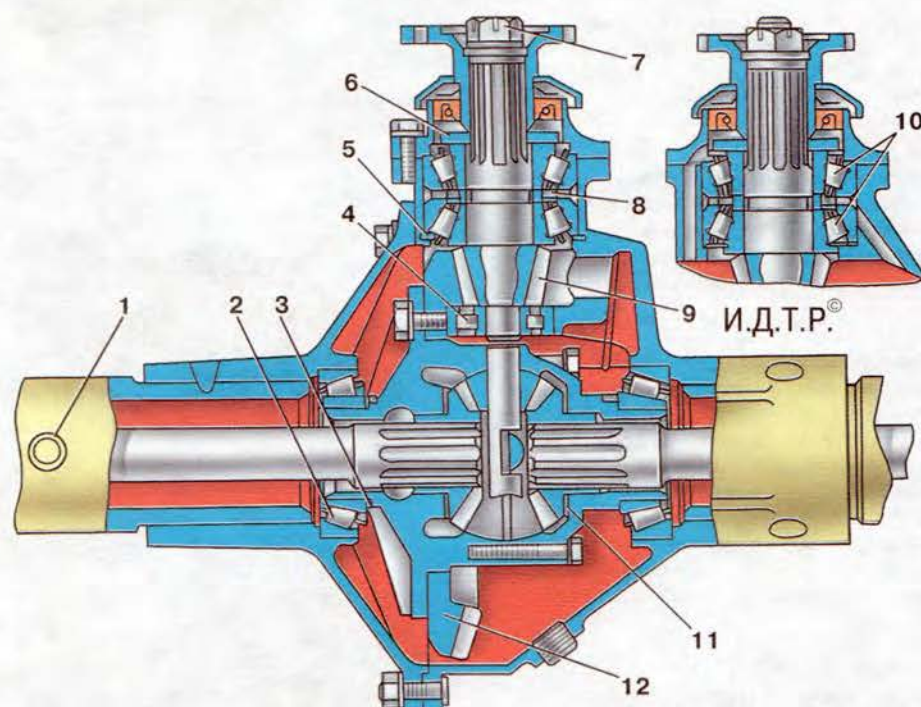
Редуктор заднего моста с разъемным картером: 1 – сапун; 2 – подшипник дифференциала; 3, 8 – регулировочные прокладки; 4 – задний подшипник ведущей шестерни; 5 – кольцо; 6 – манжета; 7 – гайка; 9 – ведущая шестерня главной передачи; 10 – передний подшипник ведущей шестерни; 11 – упорная шайба; 12 – ведомая шестерня главной передачи
